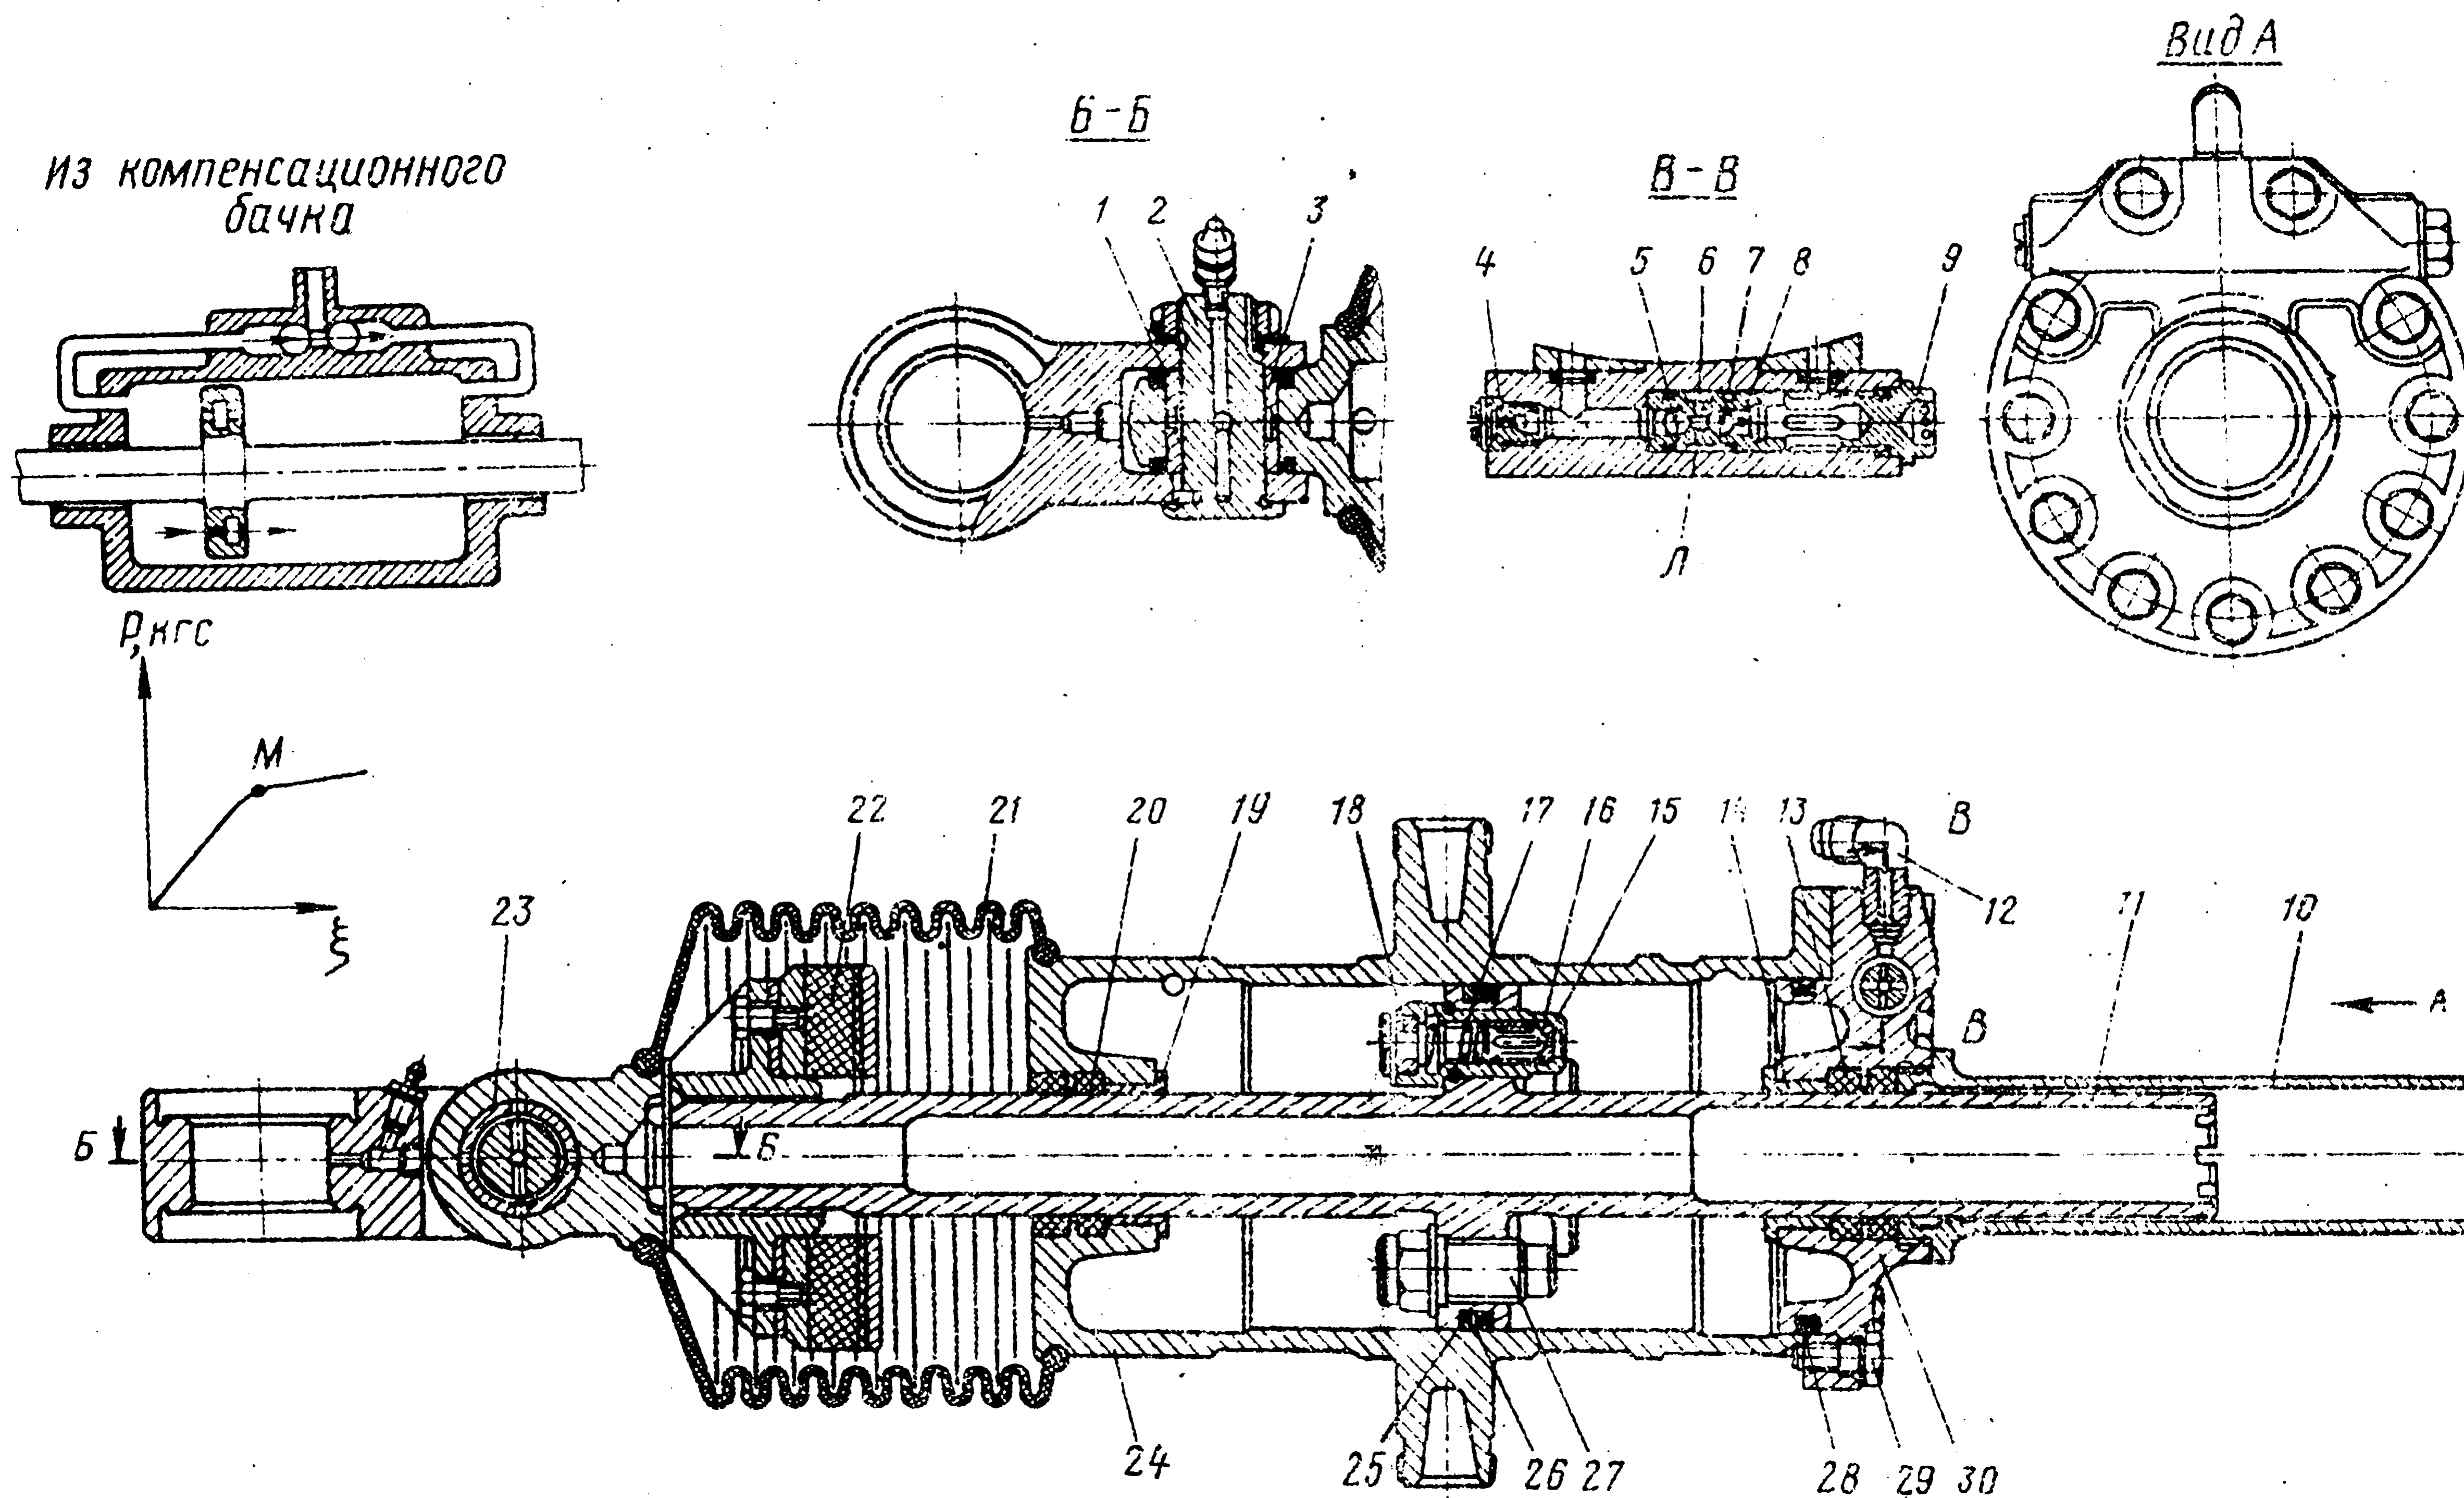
Гидравлический демпфер втулки несущего винта: 1, 14, 19 — бронзовые втулки; 2 — палец; 3, 13, 20, 28 — уплотнительные кольца; 4 — заглушка; 5, 7 — большие шарики; 6 — малый шарик; 8, 16, 27 — клапаны; 9 — пробка; 10 — стакан; 11 — шток; 12 — подсоединительный угольник; 15 — корпус перепускного клапана; 17 — пружина; 18 — гайка; 21 — чехол; 22 — амортизатор; 23 — корпус упора; 24 — цилиндр; 25 — цапфа; 26 — поршневые кольца; 29 — болт; 30 — крышка
